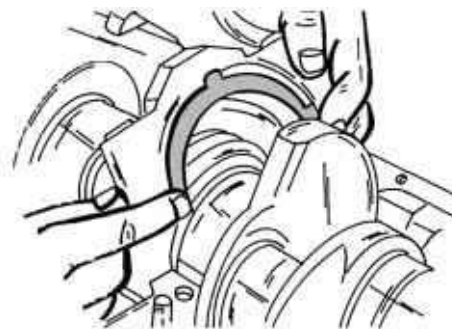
Установка кришки корінного підшипника разом із упорним півкільцем регулювання осьового зазору колінчастого вала
